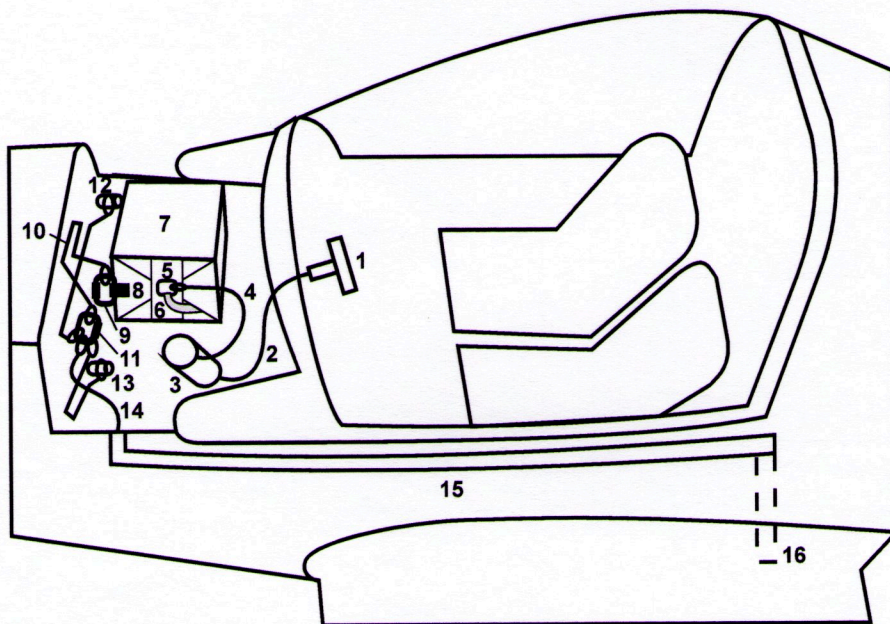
Einbau Rettungssystem, Rumpfansicht von links
